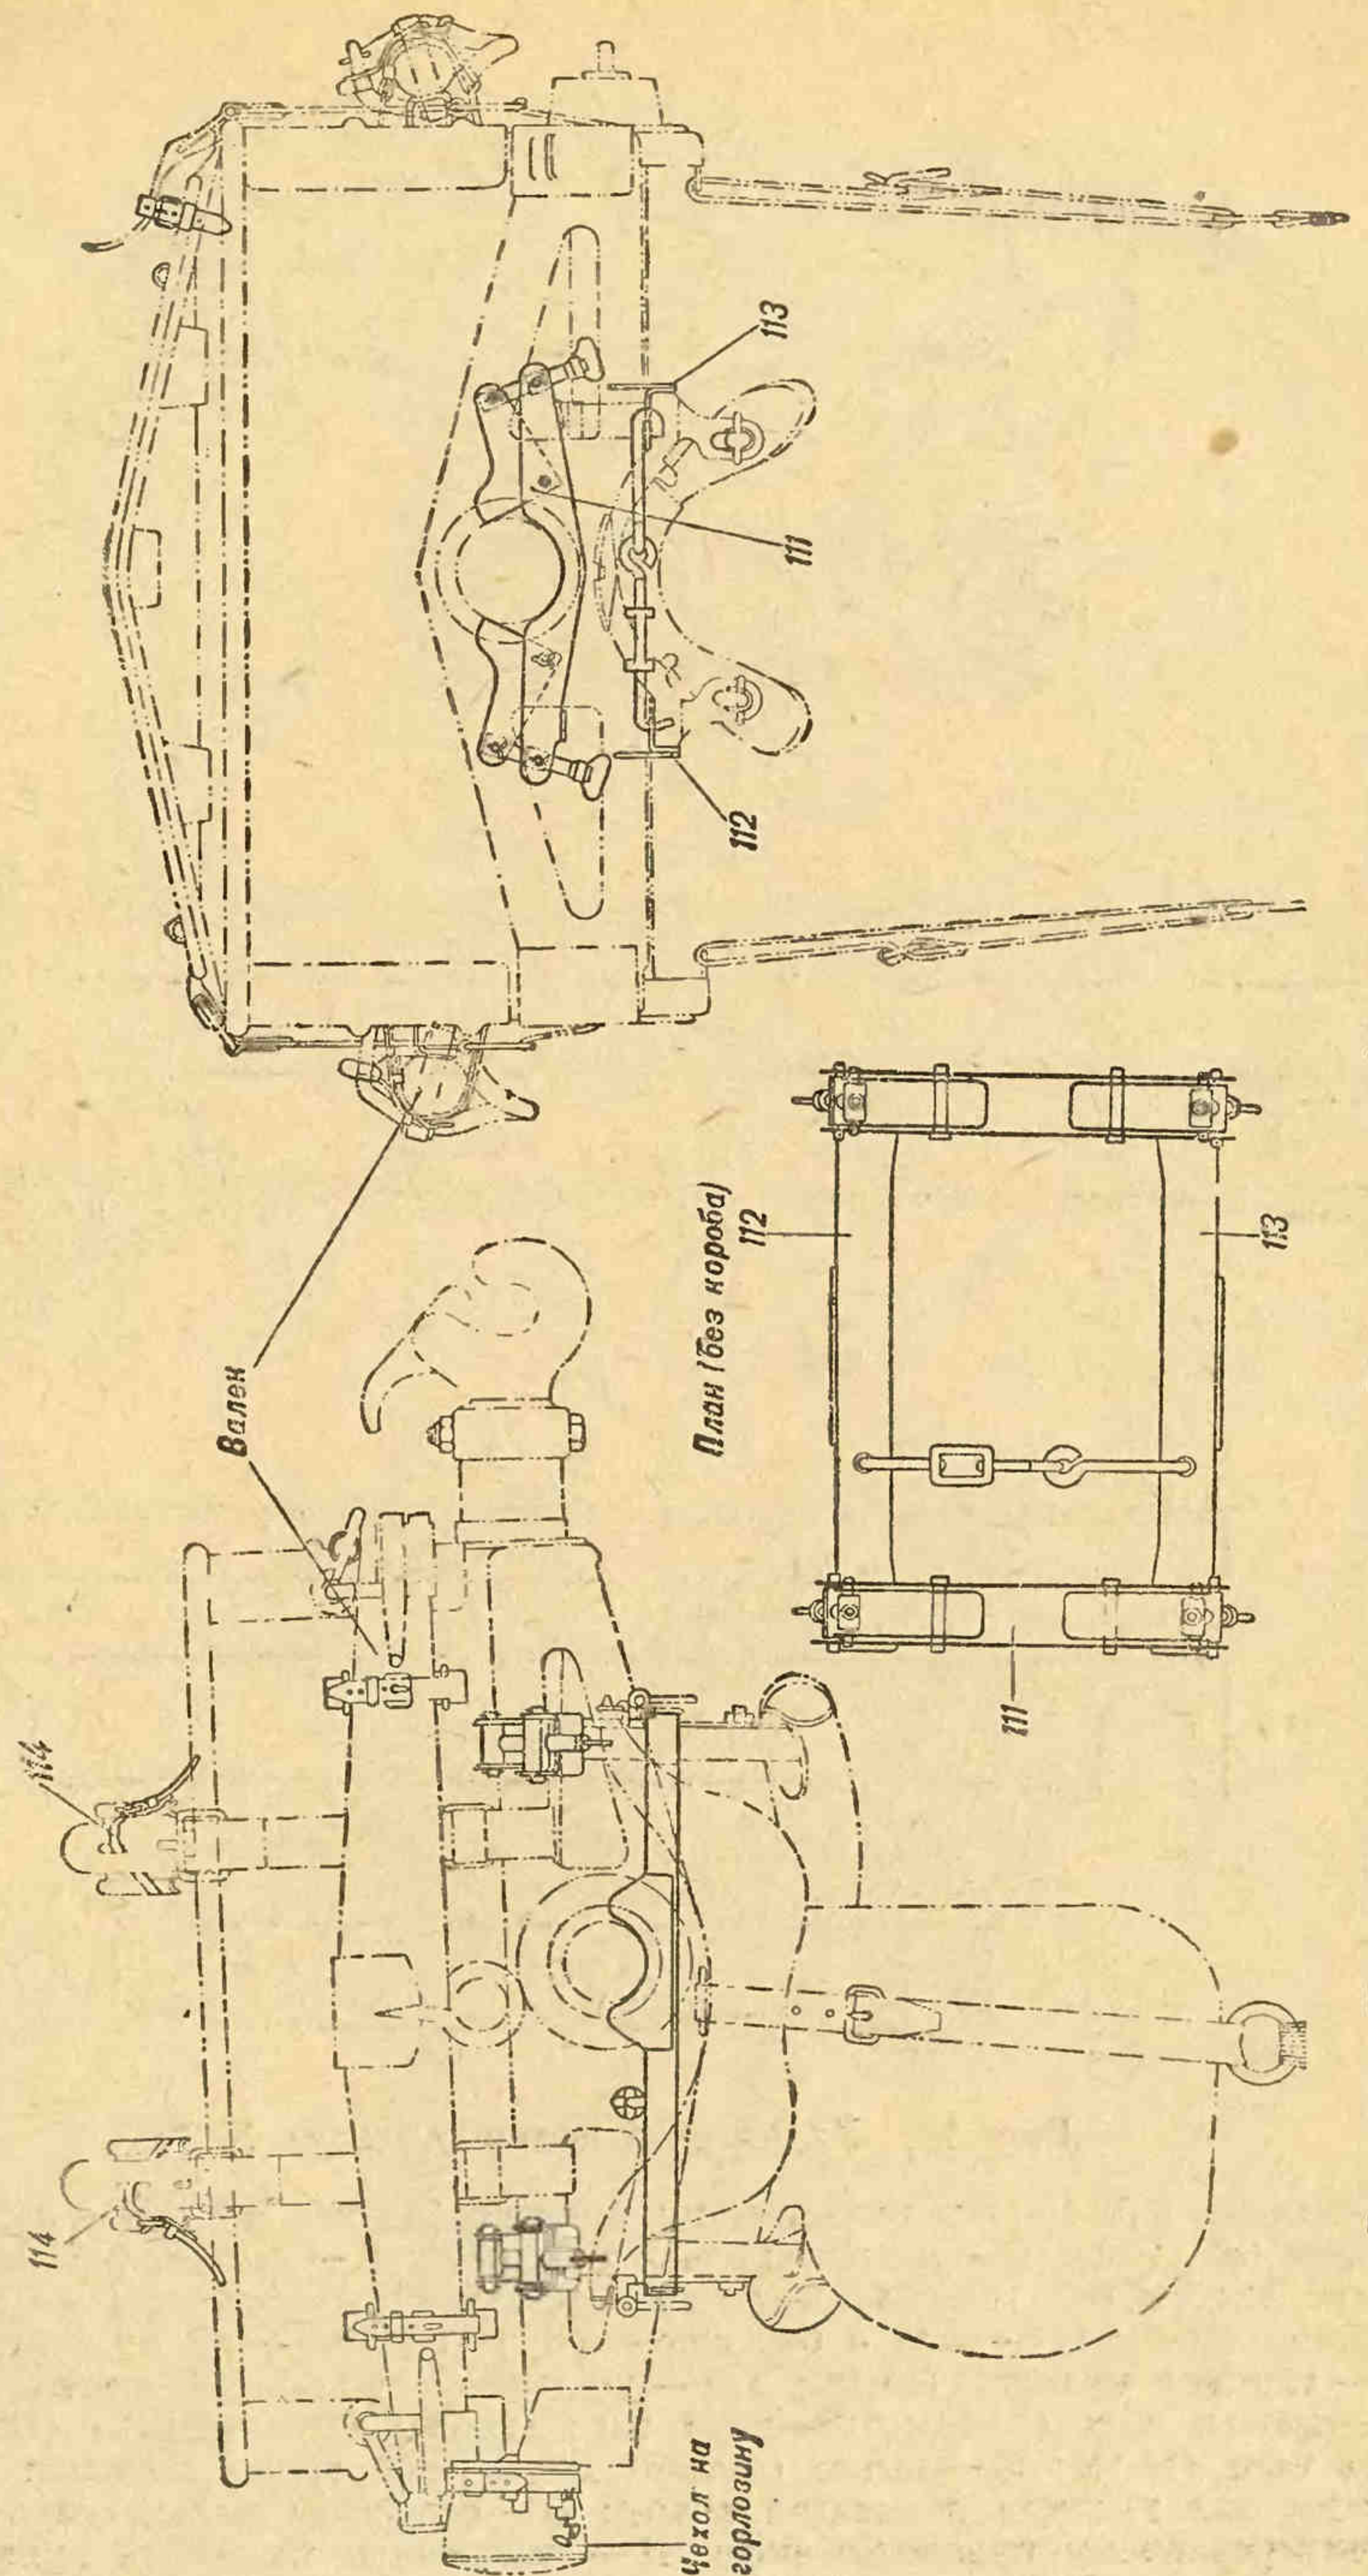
Укладочное приспособление № 7 для короба и двух вальков: 111 — ладыга (сб. 19-2); 112 — правая ладыга (сб. 19-3); 113 — левая ладыга (сб. 19-4); 114 — ремень (сб. 19-7).
